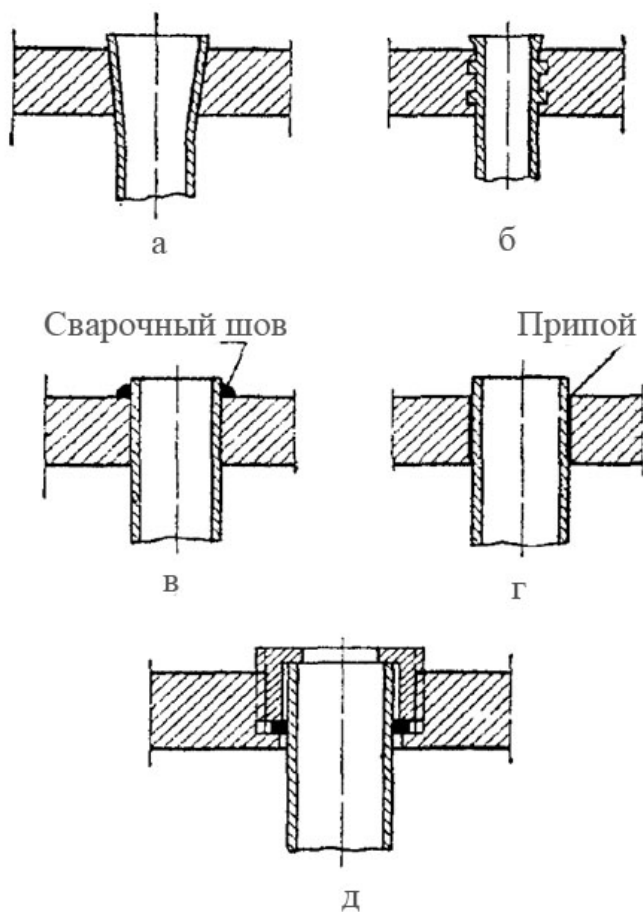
Закрепление труб в трубных решетках: а – развальцовкой; б – развальцовкой с канавками; в – сваркой; г – пайкой; д – сальниковыми устройствами
